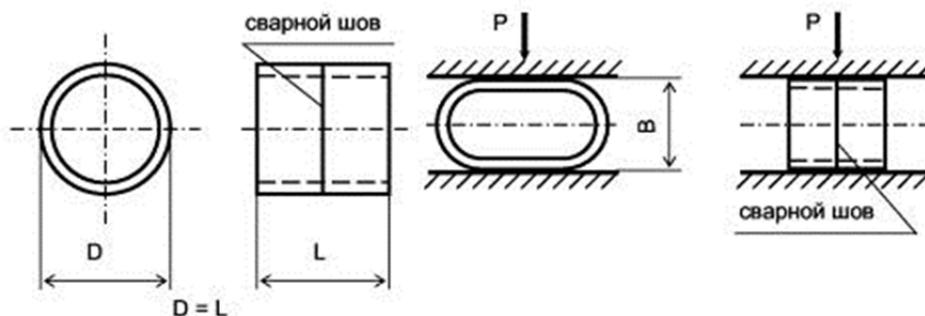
Эскиз трубчатого образца для испытаний на сплющивание и схема испытаний
